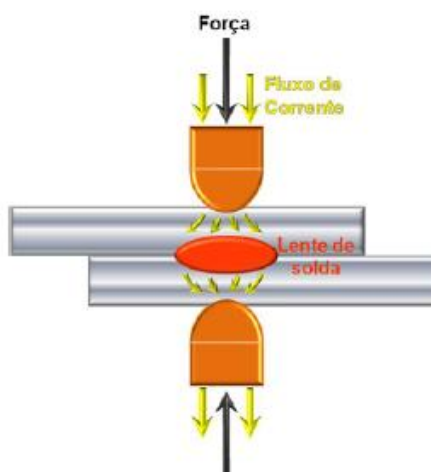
Esboço do processo de soldagem com a formação da lente de solda.
